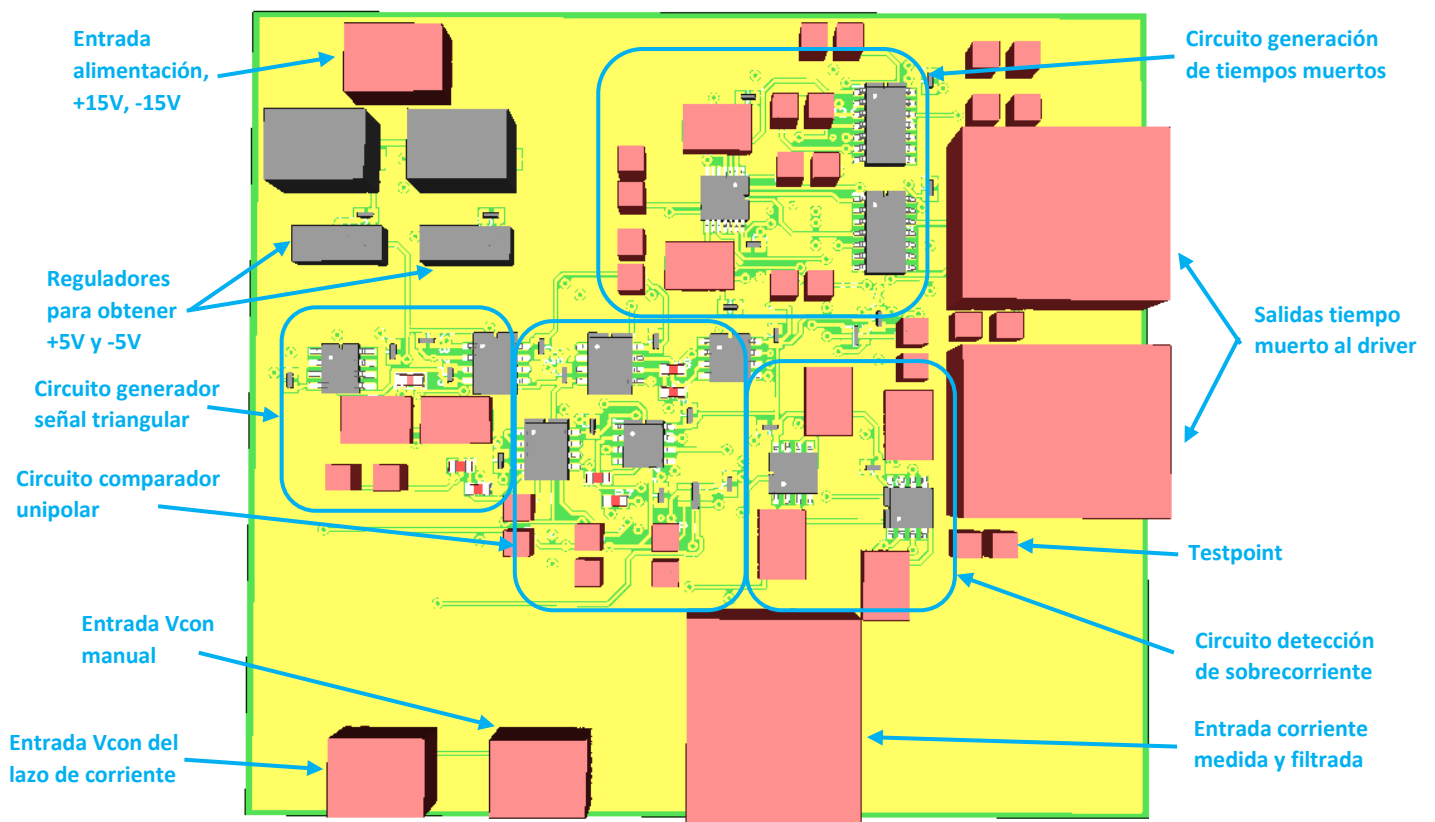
Diseño 3D de la placa PCB del circuito de modulación
